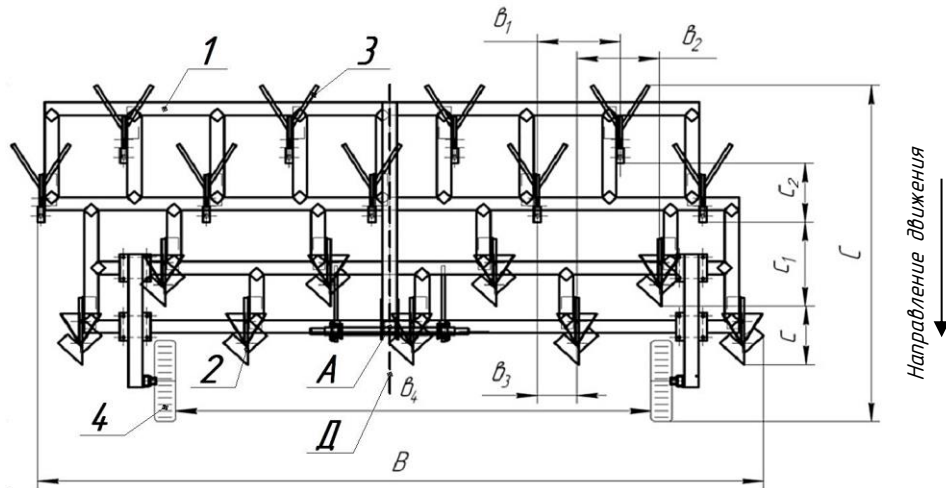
Конструктивно-технологическая схема почвообрабатывающего орудия КОМБИ-6: 1 – рама; 2 – рыхлительный рабочий орган; 3 – чизельный рабочий орган; 4 – опорное колесо с механизмом регулировки глубины; А – точка прицепа почвообрабатывающего орудия; Д – линия тяги трактора; В – ширина захвата орудия (6,3 м); С – длина орудия (3,2 м);  $v_1$  – расстояние между чизельными рабочими органами в ряду (0,7 м);  $v_2$  – расстояние между рыхлительными рабочими органами в ряду (0,7 м);  $v_3$  – расстояние между рыхлительными и чизельными рабочими органами в ряду (0,35 м);  $v_4$  – расстояние между опорными колесами (4,0 м);  $c$  – расстояние между рыхлительными рабочими органами по ходу (0,6 м);  $c_1$  – расстояние между рыхлительными и чизельными рабочими органами по ходу (0,7 м);  $c_2$  – расстояние между чизельными рабочими органами по ходу (0,6 м).
